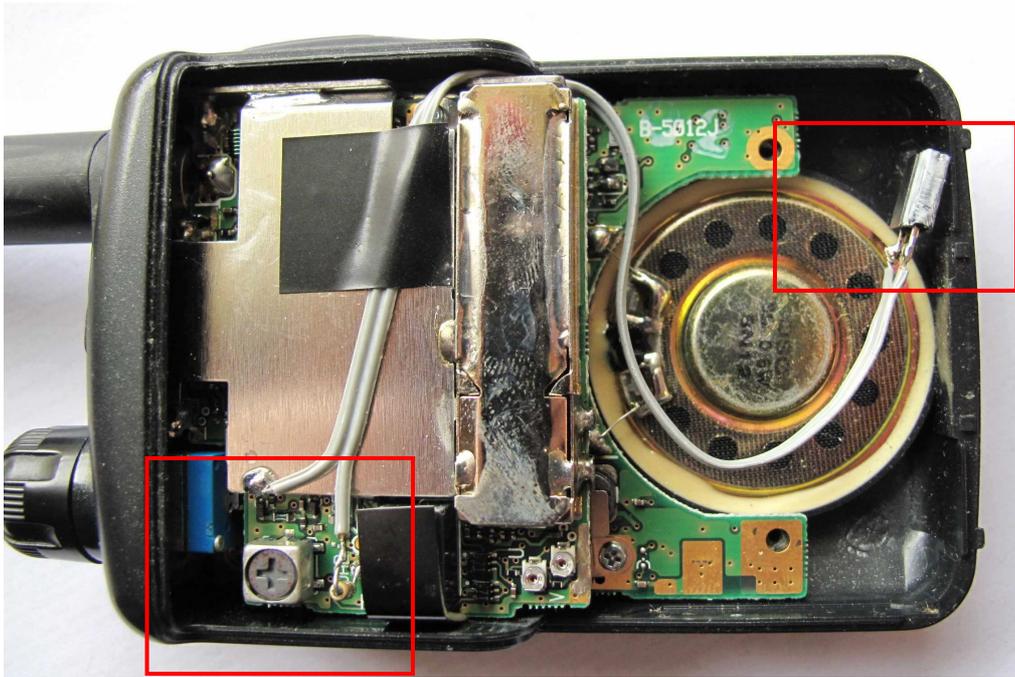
Mise en place des fils et du connecteur. Une des extrémités est soudée sur la 10 k Ω et l'autre à la masse sur le blindage. A l'autre extrémité est soudé un connecteur de type HE14. Le point actif a été peint en blanc pour le reconnaître de la masse en noir.
